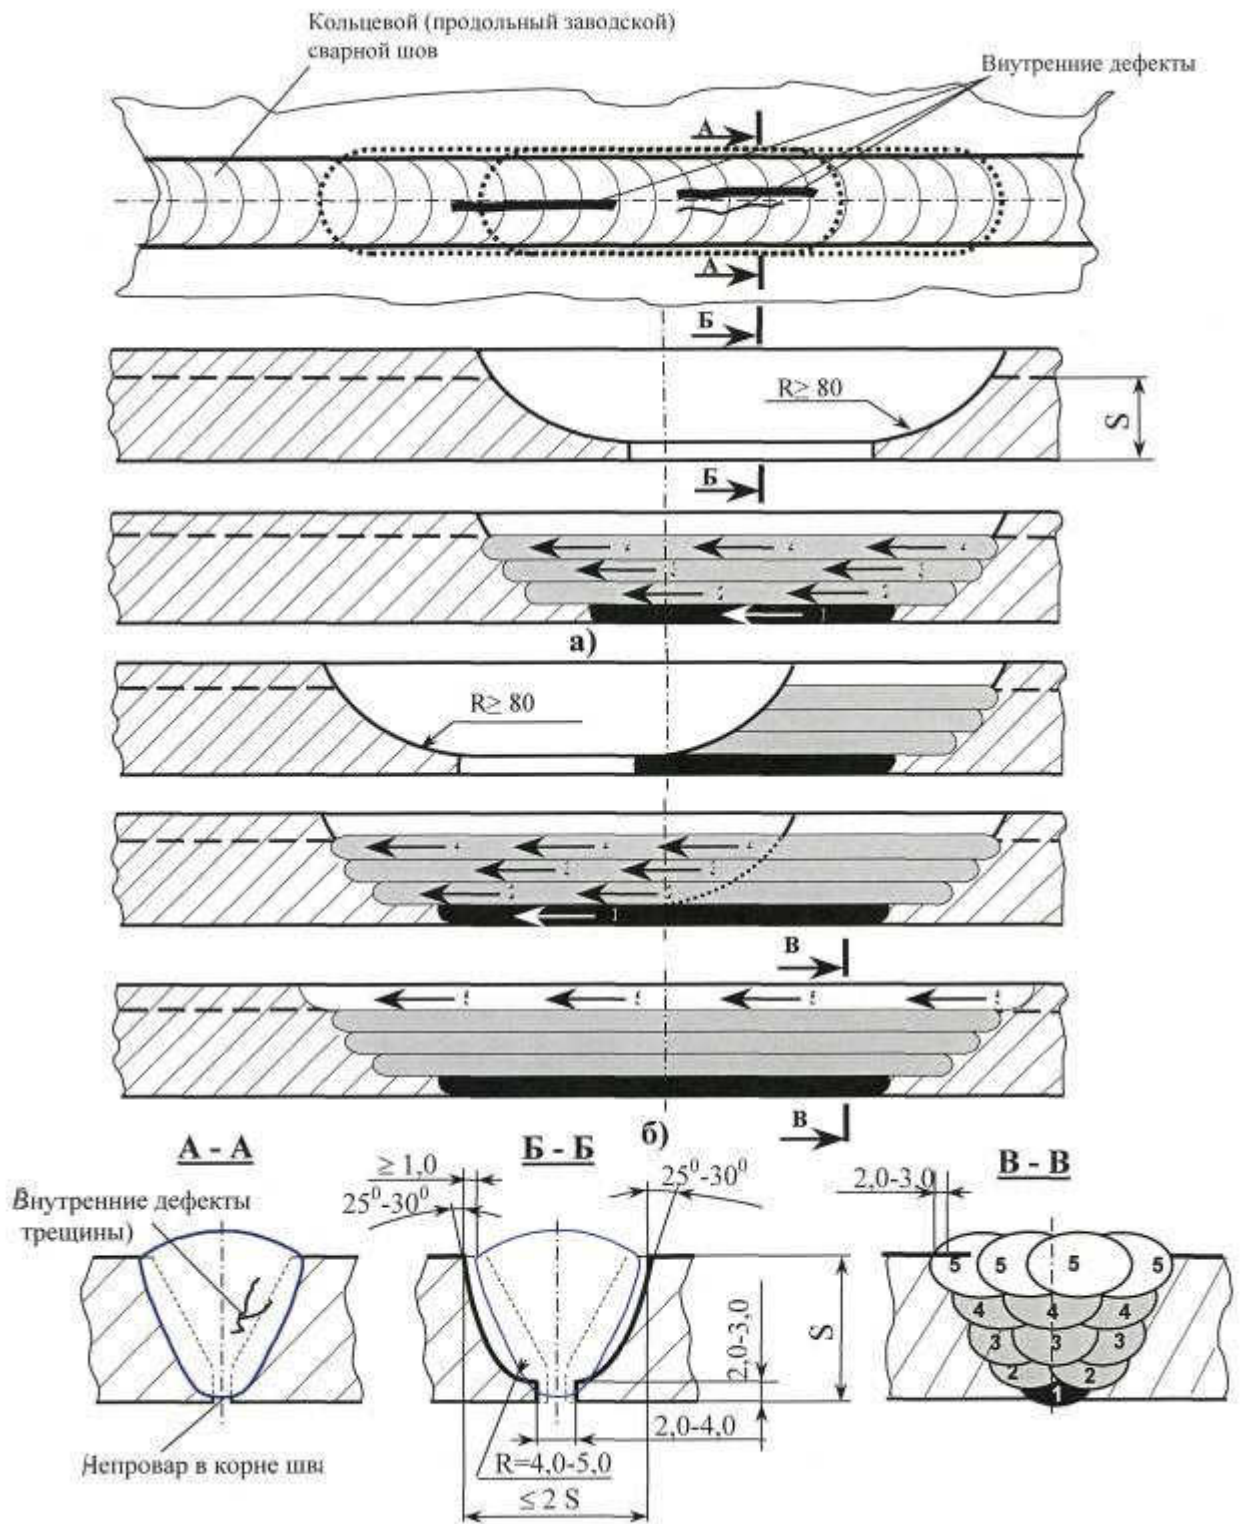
Параметры выборки дефектного участка, последовательность и направление слоев шва при сварке (заварке) сквозной выборки прямолинейной формы длиной до 250 мм (а,б – первый и второй этапы выборки и сварки)
